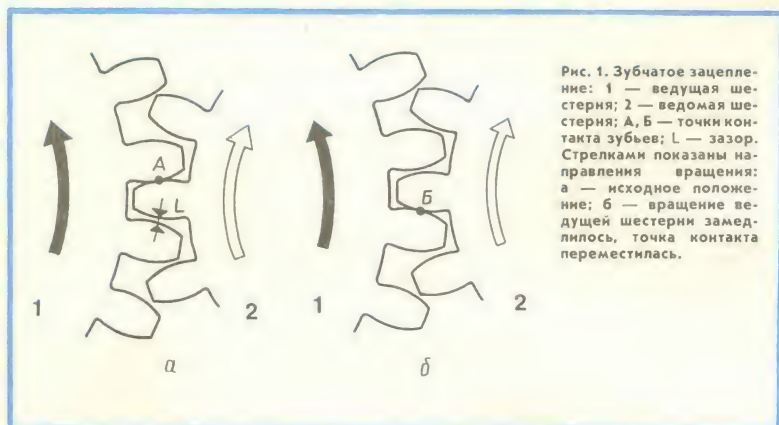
Зубчатое зацепление: 1 — ведущая шестерня; 2 — ведомая шестерня; А, Б — точки контакта зубьев; L — зазор. Стрелками показаны направления вращения: а — исходное положение; б — вращение ведущей шестерни замедлилось, точка контакта переместилась.
